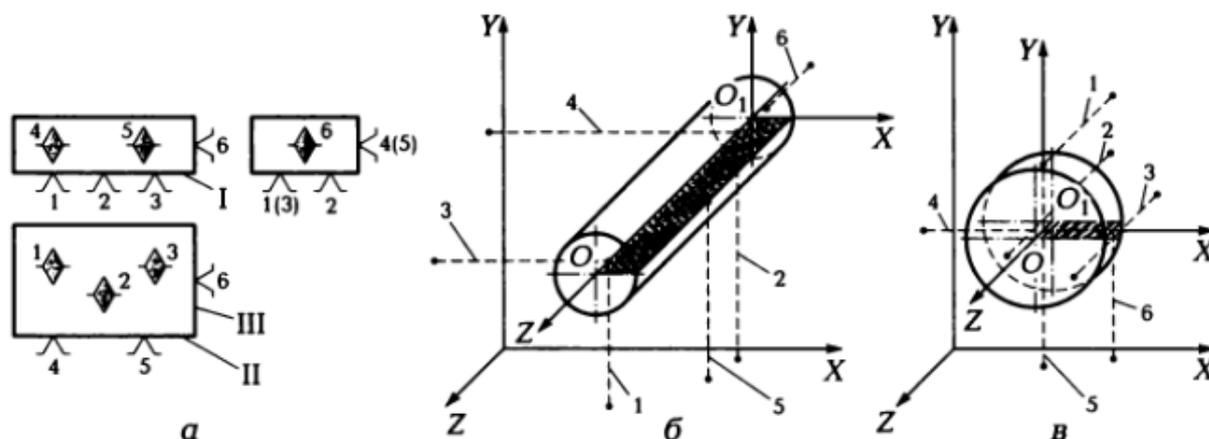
Схема расположения опорных точек и комплекты баз для вала и диска:
